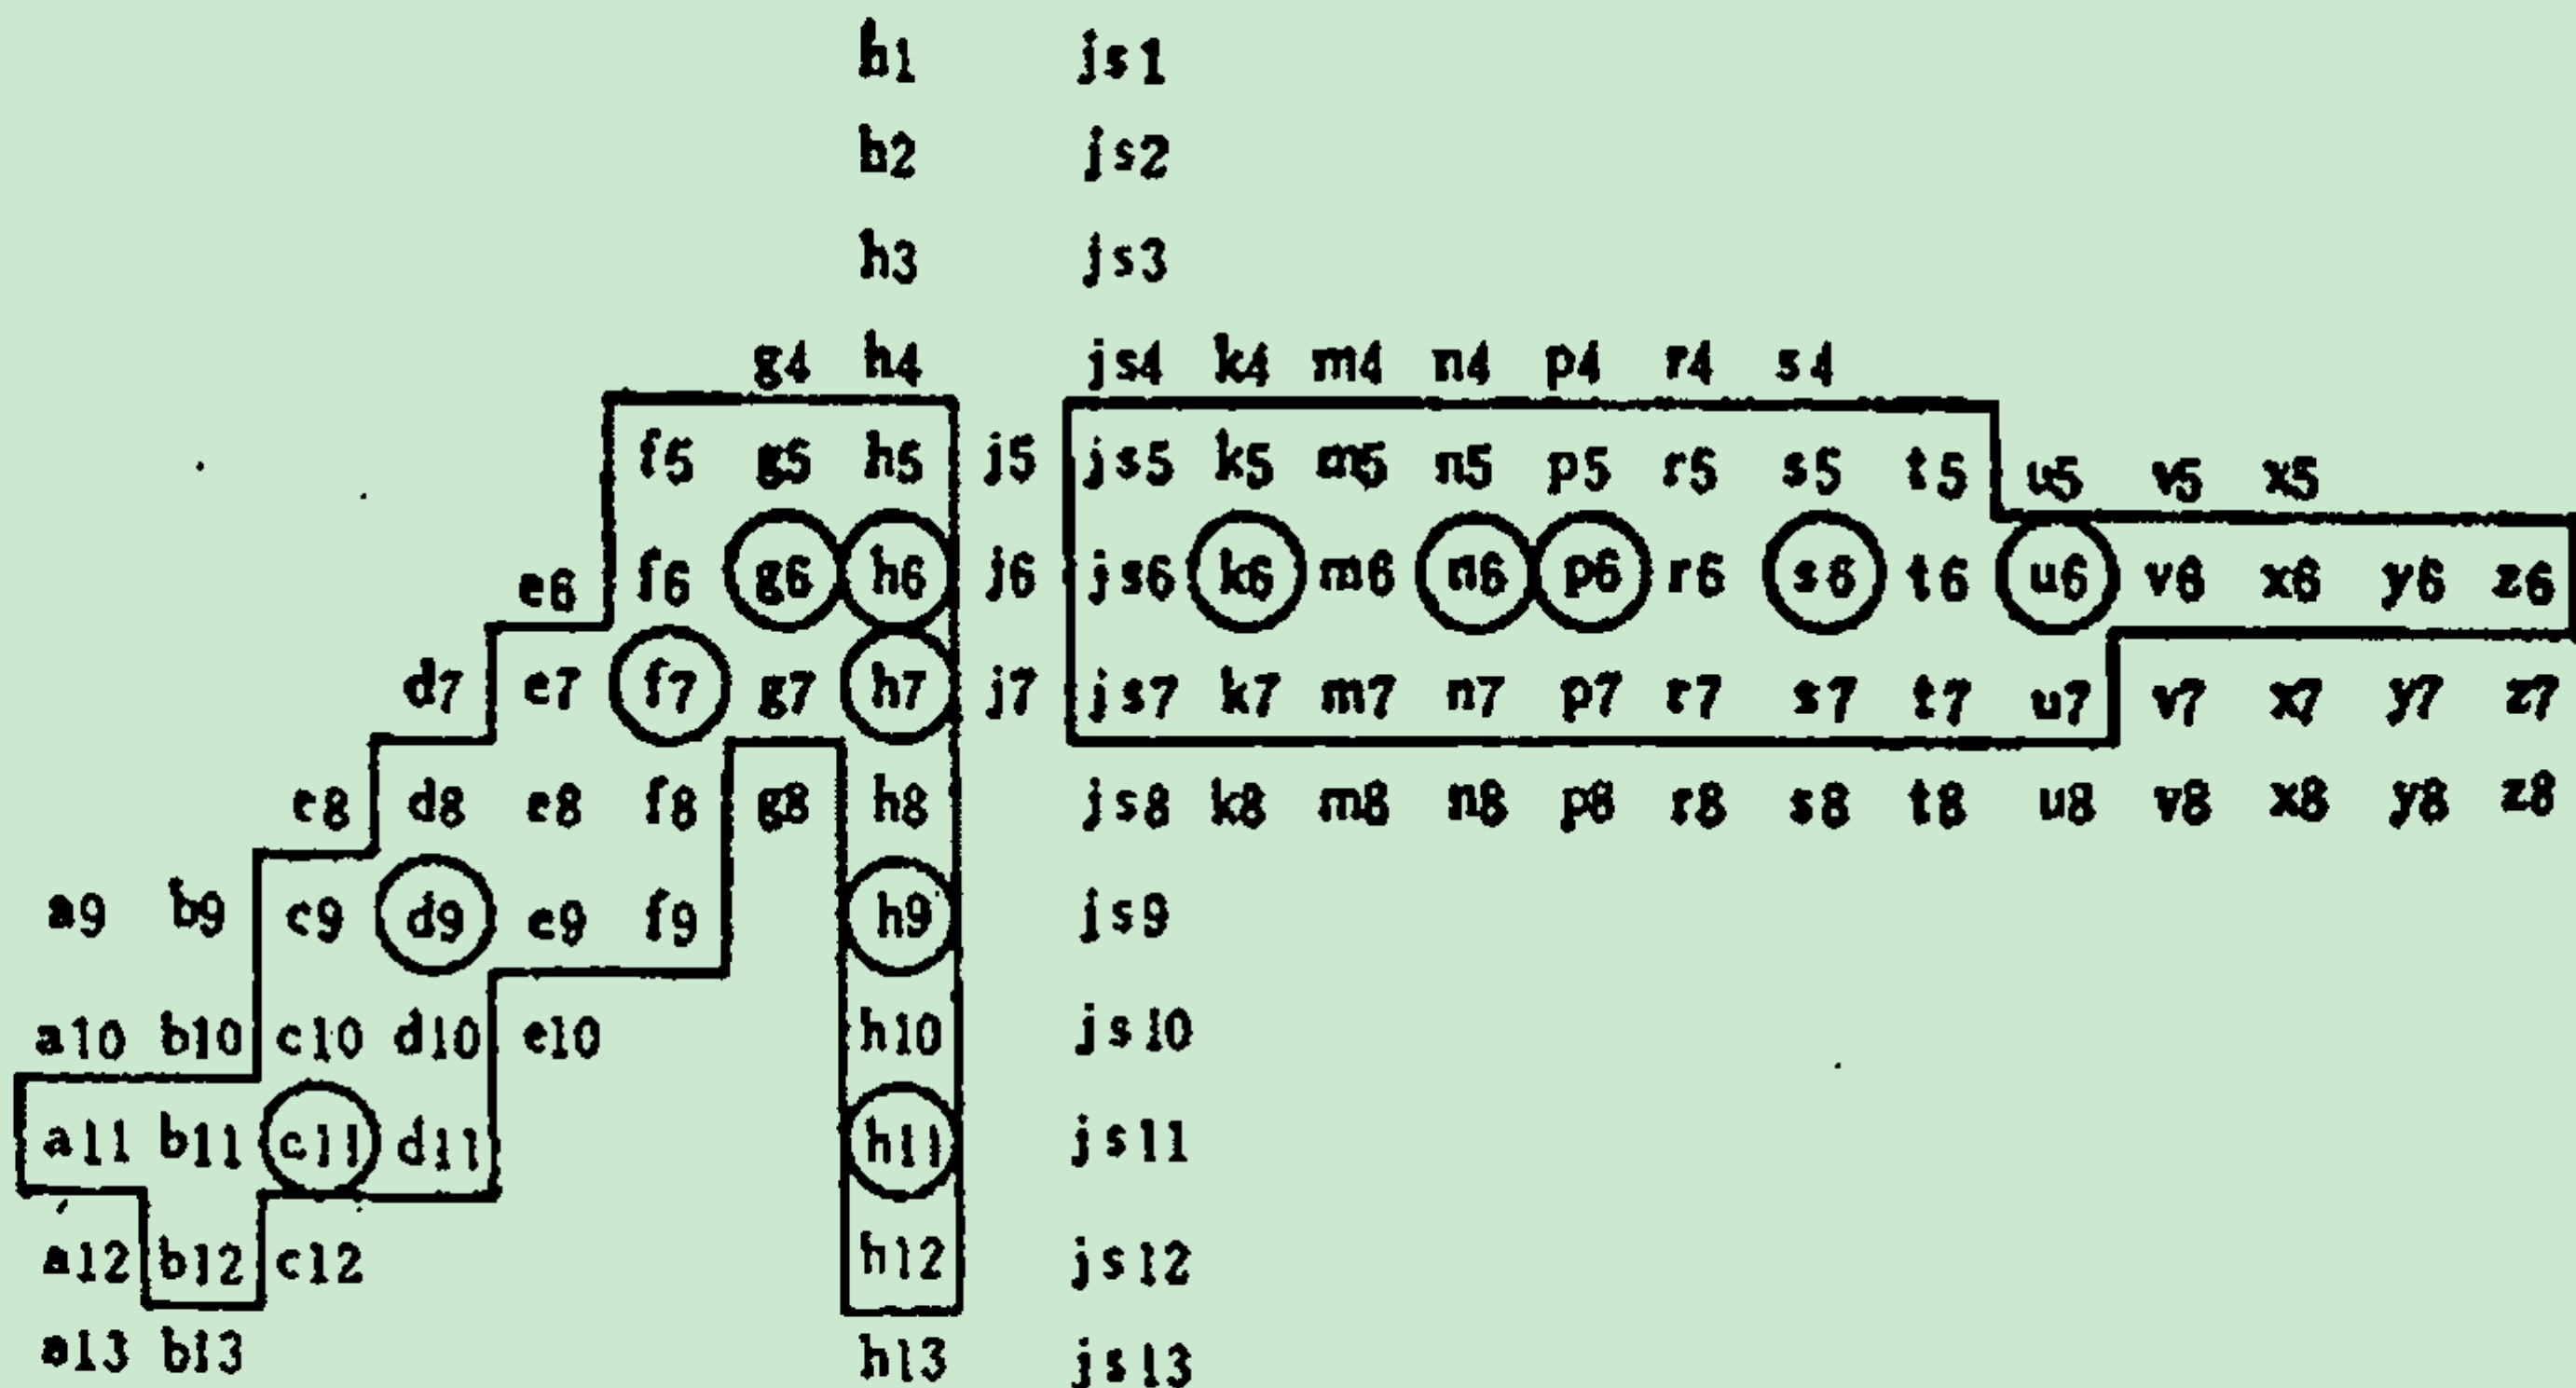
公称尺寸至 500mm 轴的常用、优先公差带
